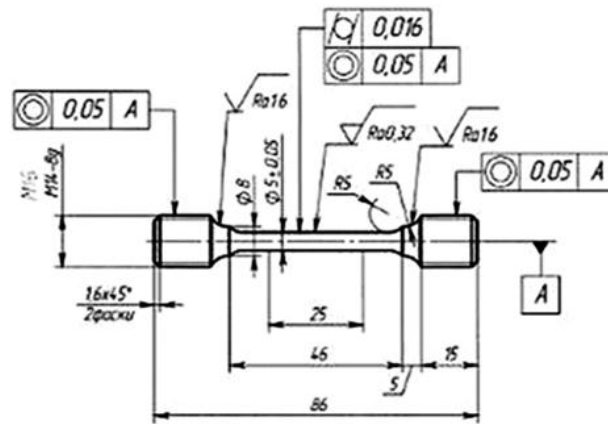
Эскиз образца, на котором исследовались поверхности разрушения
